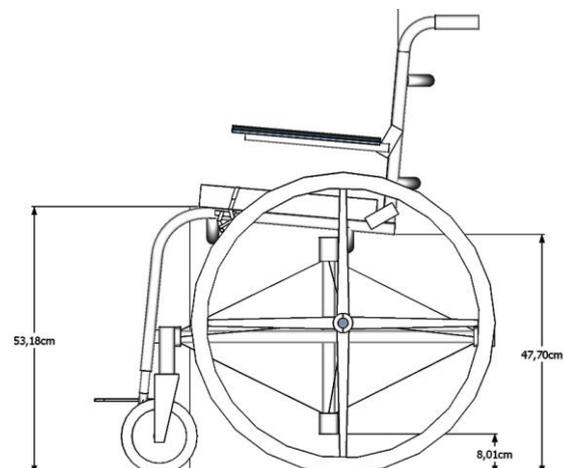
Desenho técnico cadeira de rodas *tensegrity* – vista lateral
